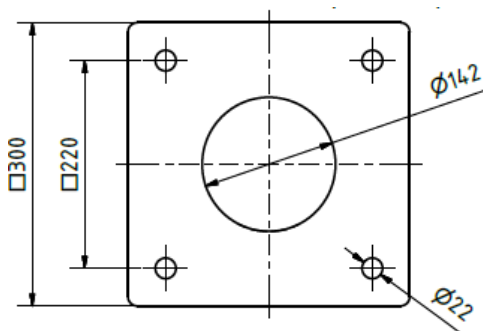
Flanschplatte Poller mit Bohrungen (4x)
